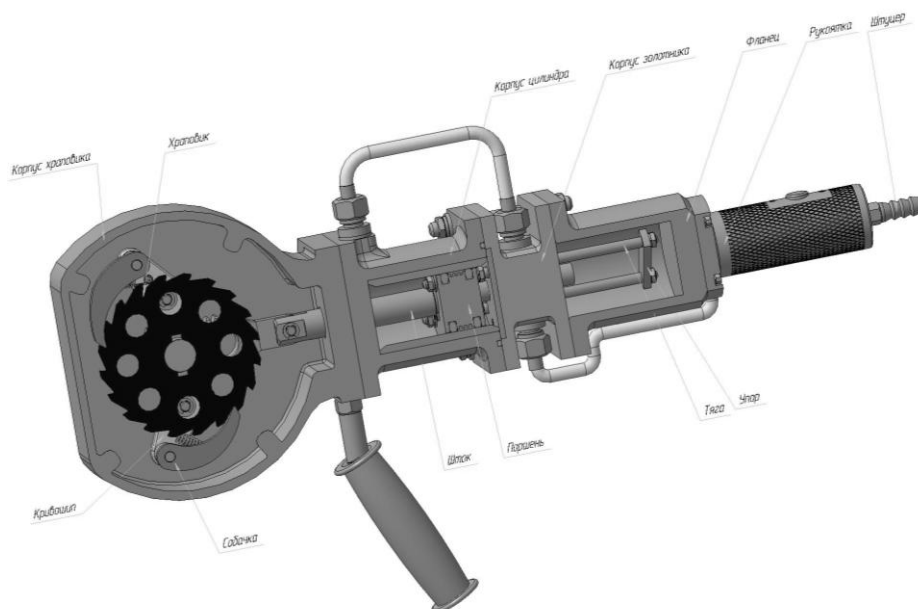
Схема модернизированного пневматического поршневого гайковерта
